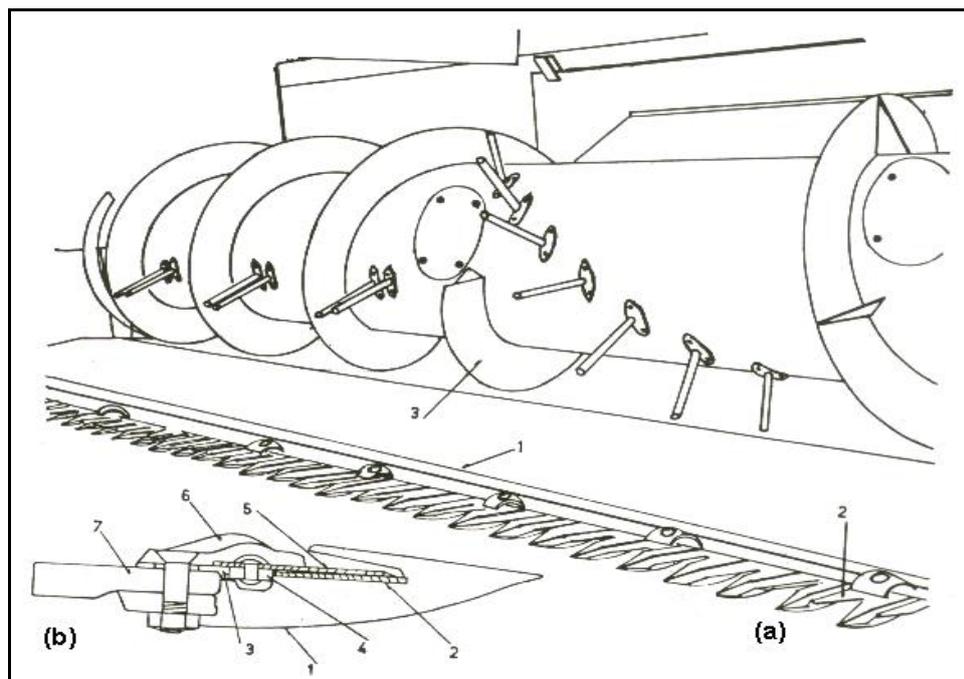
Barra de corte de uma colhedora: a) vista geral de uma barra de corte: 1) barra; 2) faca; 3) condutor helicoidal; b) detalhe de construção da barra: 1) guarda; 2) placa de apoio; 3) placa de desgaste; 4) barra da faca; 5) seção da faca; 6) grampo; 7) barra de suporte.
